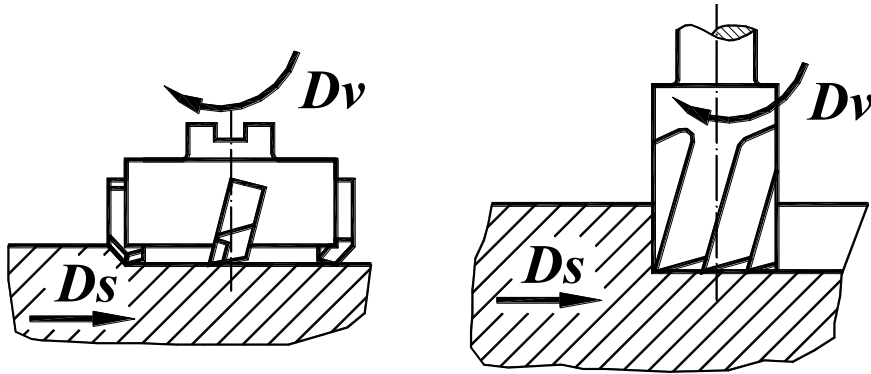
Торцеве фрезерування (насадними, кінцевими фрезами). Dv – головний рух інструменту, Ds – рух подачі.
